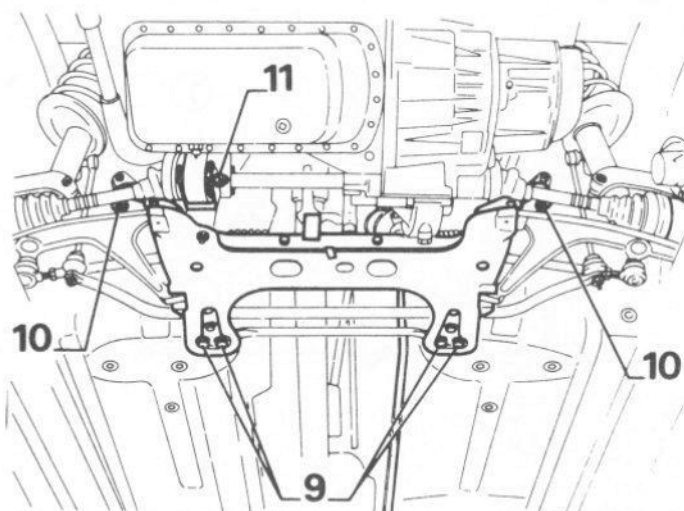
Il faut abaisser le faux-châssis avant pour pouvoir déposer le boîtier de direction assistée (Sec 20)
